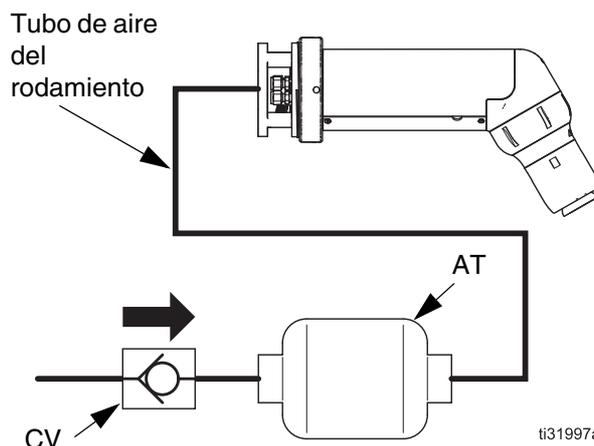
Tubo de aire del rodamiento con tanque acumulador y válvula de retención
